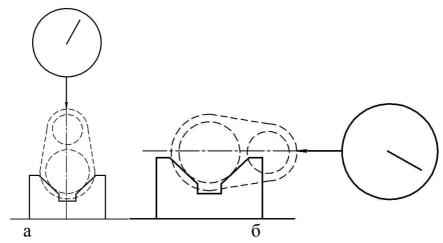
Схема приспособления для проверки величины эксцентриситета ступенчатого валика
